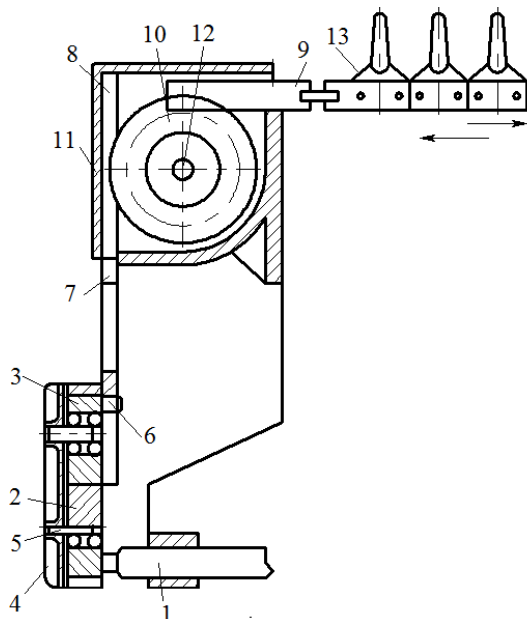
Общий вид эксцентрикового привода режущего аппарата
